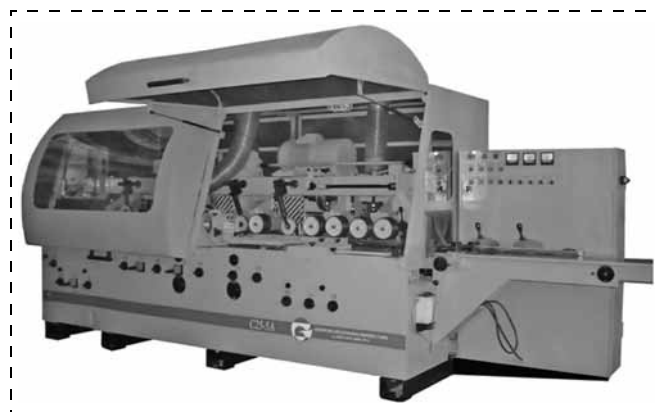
Станок четырехсторонний продольно-фрезерный шестишпиндельный С25-5А
